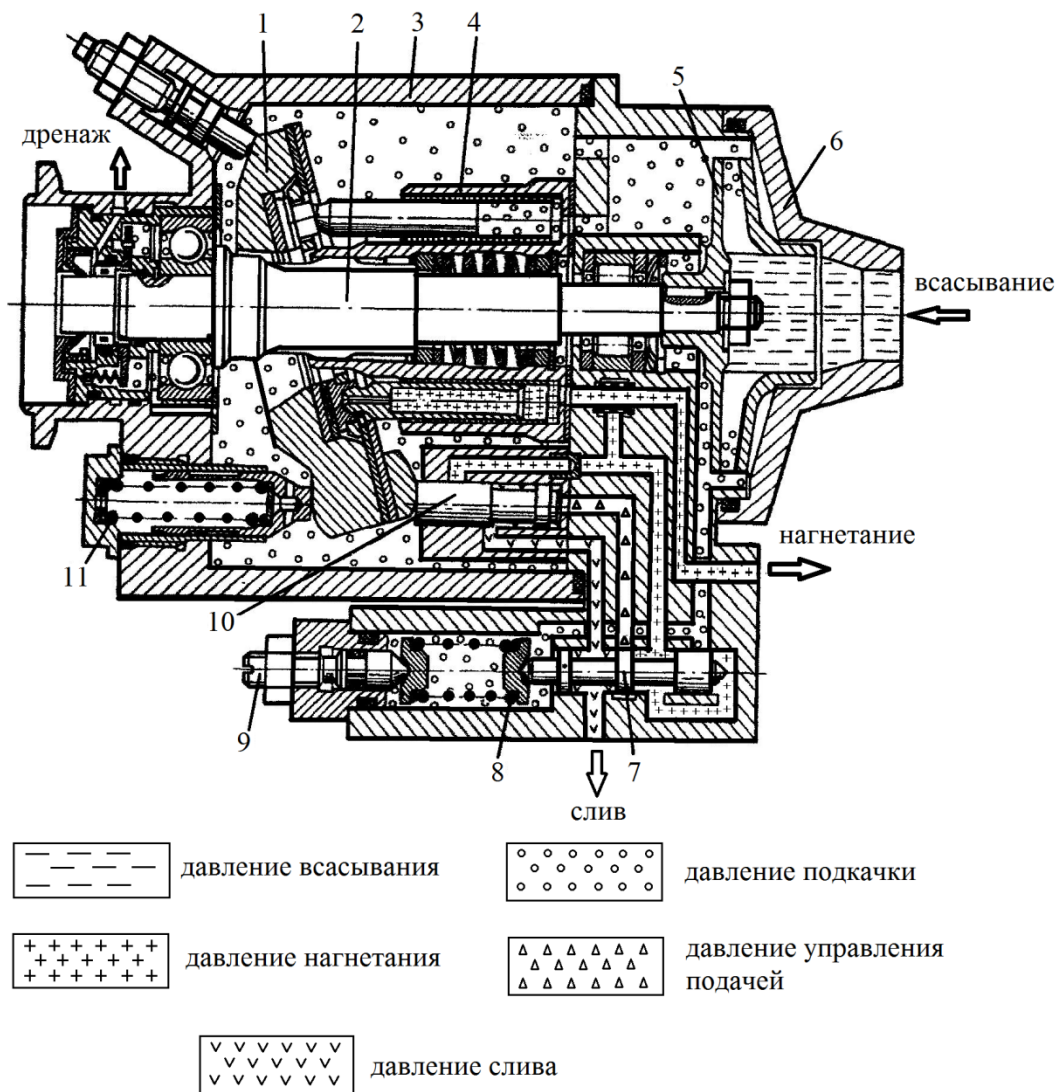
Схема работы насосной станции, где 1- опорная шайба; 2- вал; 3- корпус; 4- блок цилиндров; 5- крыльчатка подкачивающего насоса; 6- крышка; 7- золотник; 8, 11- пружина; 9- регулировочный винт; 10- поршень
